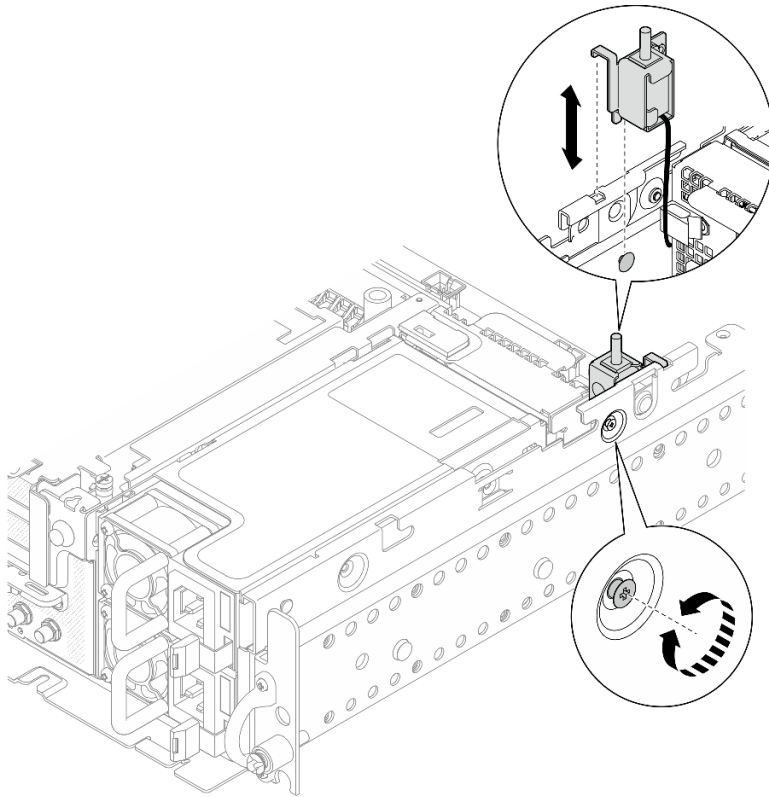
Installieren des Schalters gegen unbefugten Zugriff mit Kabel
